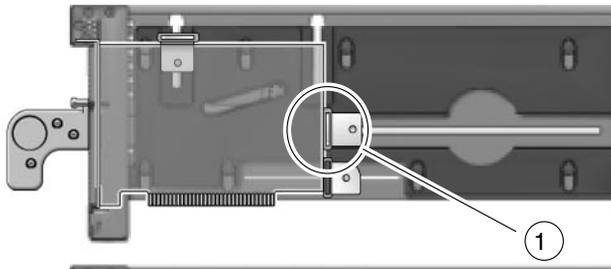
Utilisation d'un verrou de carte pour fixer la carte PCI
